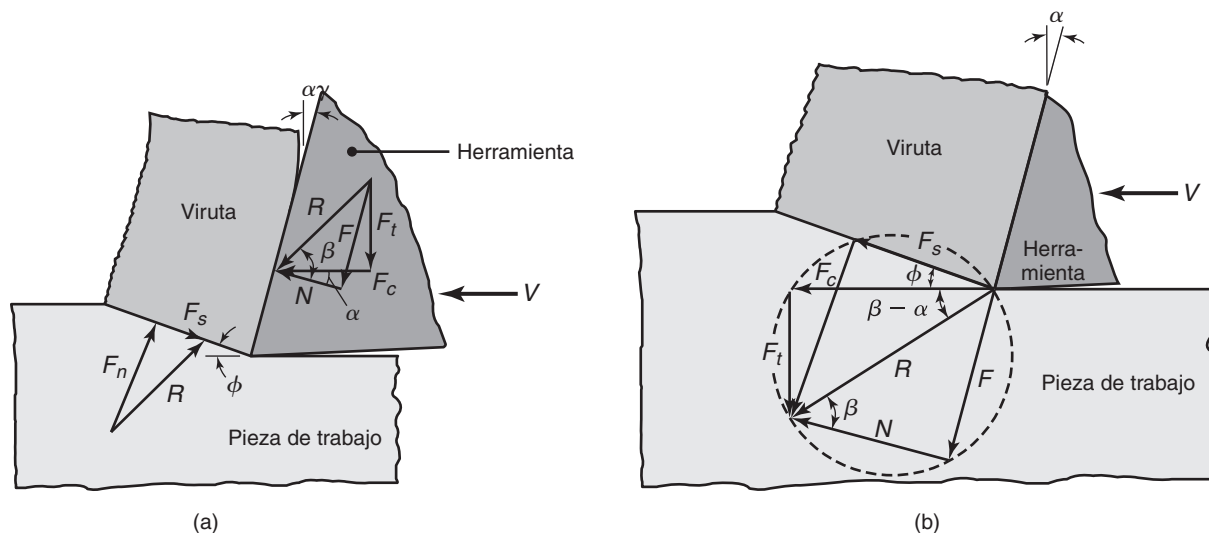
(a) Fuerzas que actúan en la zona de corte durante el corte bidimensional. Obsérvese que la fuerza resultante, R , debe ser colineal para equilibrar las fuerzas. (b) Círculo de fuerzas para determinar las diferentes fuerzas que actúan en la zona de corte.
